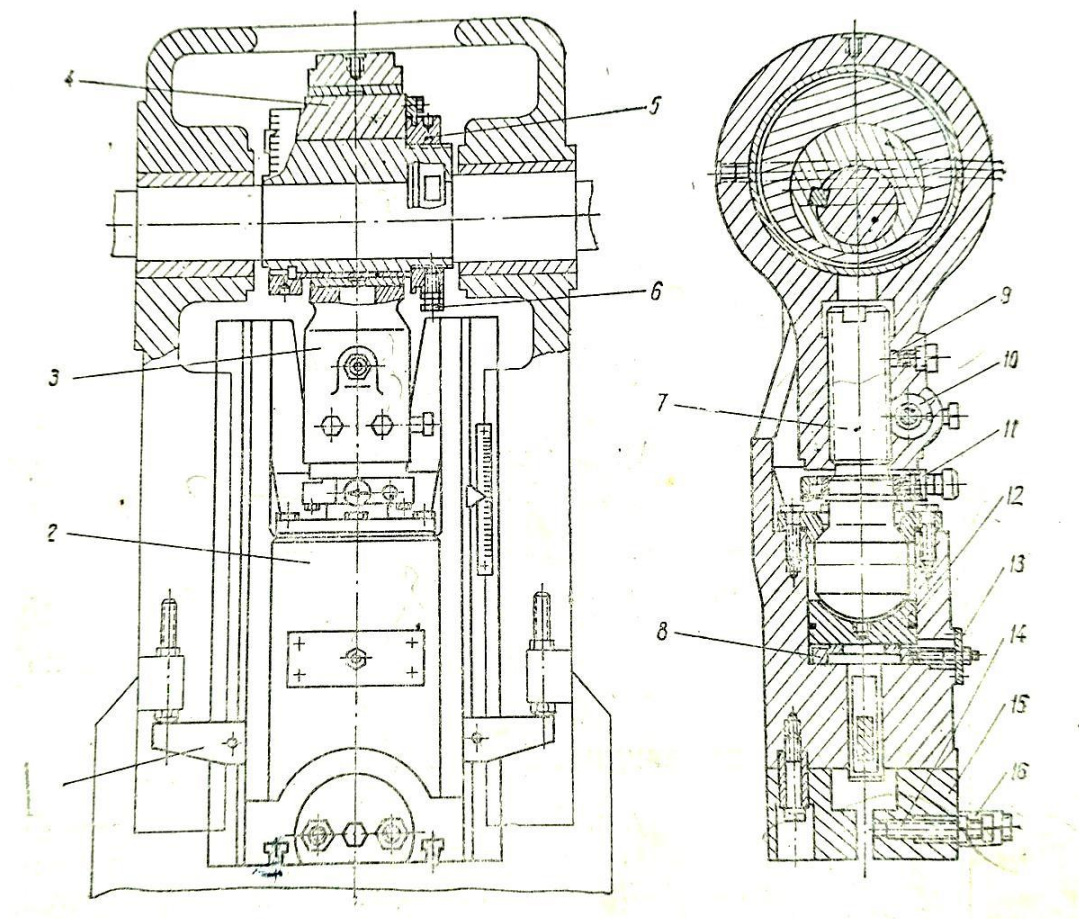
Ползун: 1- планка выталкивателя; 2- ползун; 3 – шатун; 4 – втулка эксцентриковая; 5 – гайка; 6 – фиксатор; 7 – шток; 8 – предохранитель; 9 – фиксатор; 10 – зажим; 11 – храповой механизм; 12 – подпятник; 13- крышка; 14 – винт; 15 – сухарь; 16 – гайка.
